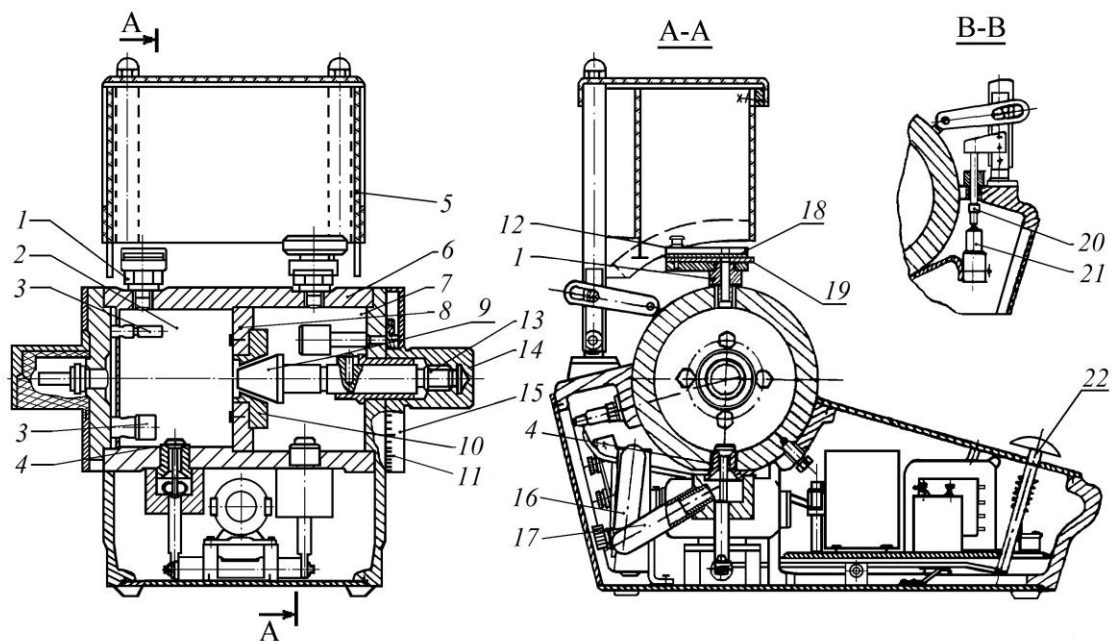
Устройство стенда ОТ 17 для определения величины тушащего зазора:
